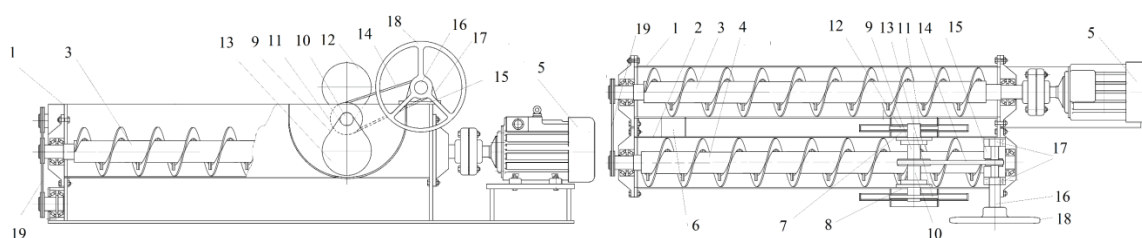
Принципиальная схема установки смесителя для производства арболита: 1,2 — корпуса; 3,4 — шнеки; 5 — электродвигатель; 6,7,8 — переходные камеры цилиндрической формы; 9 — отсекатель; 10 — вал; 11 — подшипниковый узел; 12,13 — диски цилиндрической формы; 14 — цепная передача; 15 — поворотное устройство; 16 — вал; 17 — подшипниковый узел; 18 — штурвал.
